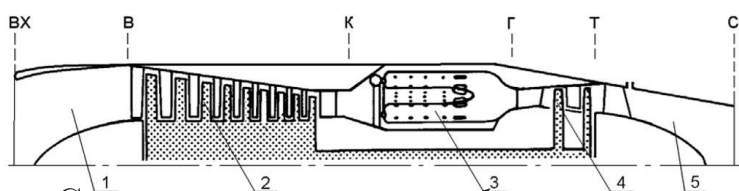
Схема одновального турбореактивного двигателя: 1 - входное устройство (воздухозаборник); 2 - компрессор; 3 - камера сгорания; 4 - турбина; 5 - выходное устройство (выходное сопло); вх, в, к, г, т, с - обозначения контрольных сечений проточной части двигателя
